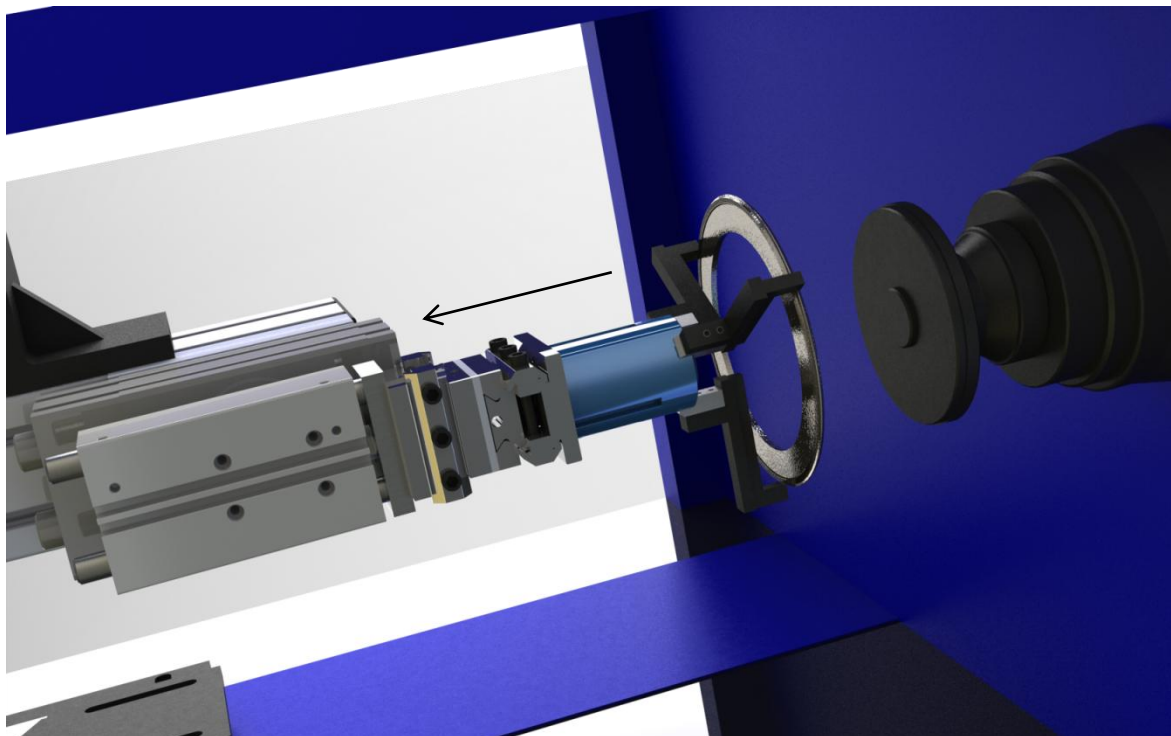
Vykládanie tesnenia z úchopovej hlavy.
